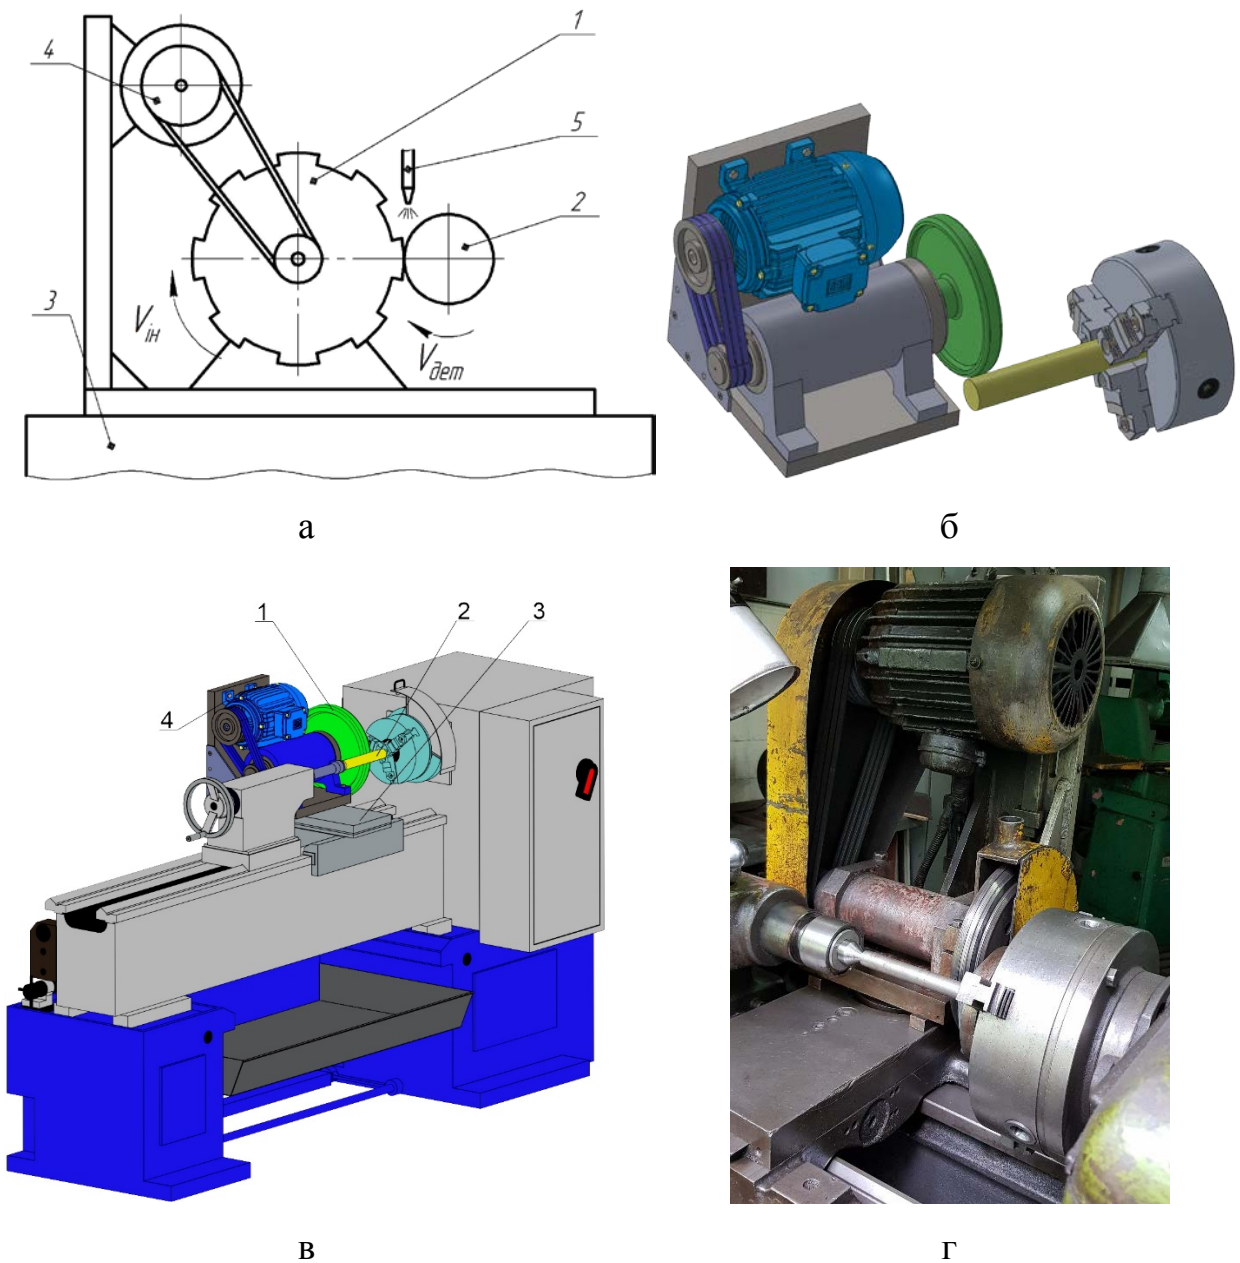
Фрикційне оброблення циліндричних поверхонь деталей машин: а – схема обробки, б – фото установки
